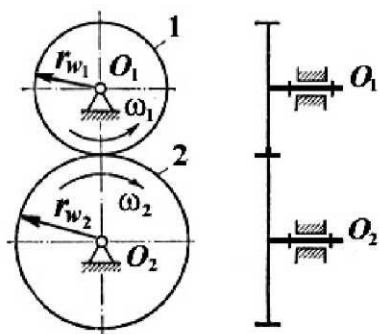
Зубчатая передача с внешним зацеплением колес
